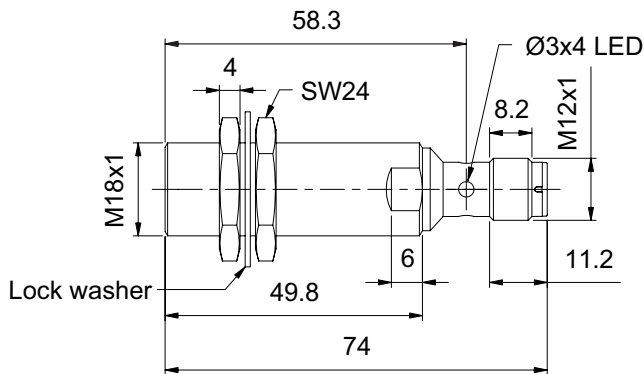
Lange Ausführung, bündiger Einbau, Steckversion
